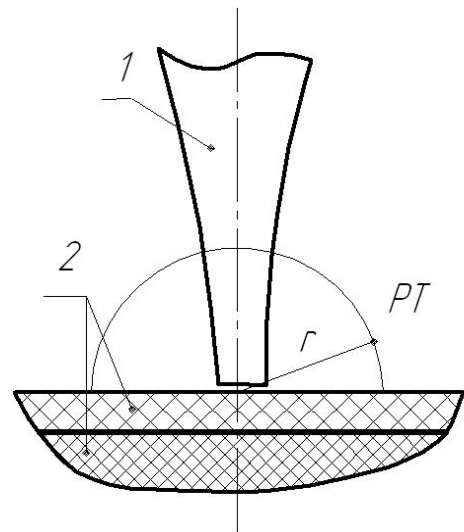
Схема ультразвуковой сварки пластмасс: 1- волновод-инструмент; 2- свариваемое изделие; РТ - расчетная точка
